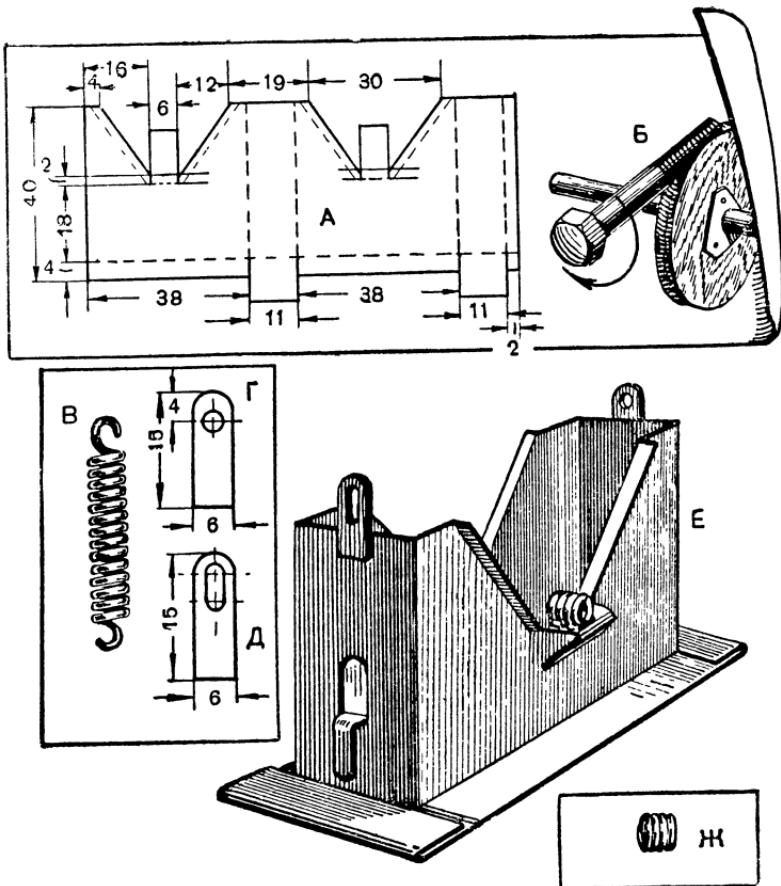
Детали червячного редуктора (рис. 124): А — развертка стенок корпуса; Б — схема изготовления зубьев червячного колеса; В — натяжная пружинка; Г и Д — подшипники для червяка; Е — корпус редуктора; Ж — подшипник червячного колеса.
